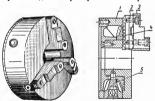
Трехкулачковый самоцентрирующий патрон: 1— корпус; 2— рейка; 3— кулачок; 4— большая коническая шестерия (диск со спиральной нареакой); 5— малая коническая шестерия;
